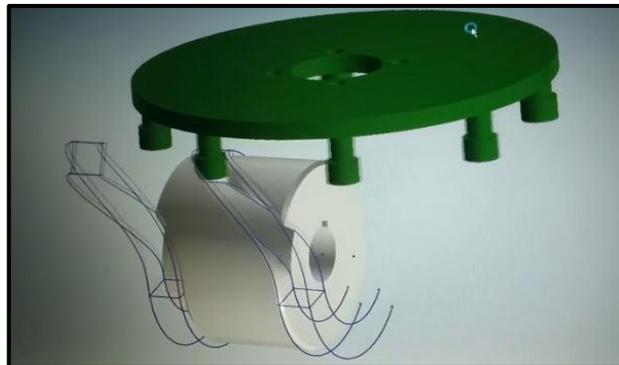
Mouvement du mécanisme et de la table index (vue 2)
